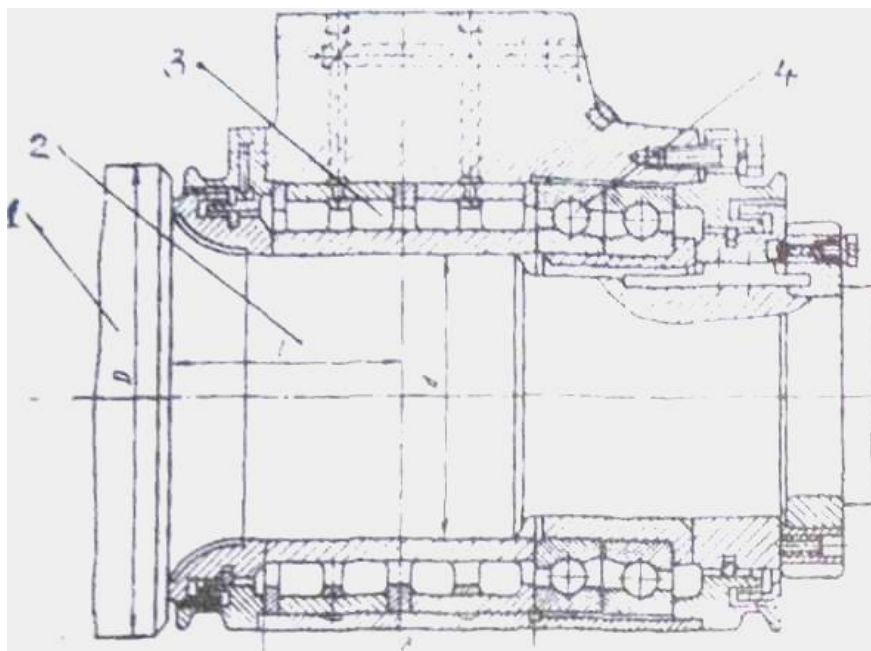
Установка підшипника з циліндричними роликами на шийці опорного валка: 1-бочка, 2-шийка, 3-чотирирядний підшипник з циліндричними роликами, 4 -кульовий радіально-упорний підшипник.
